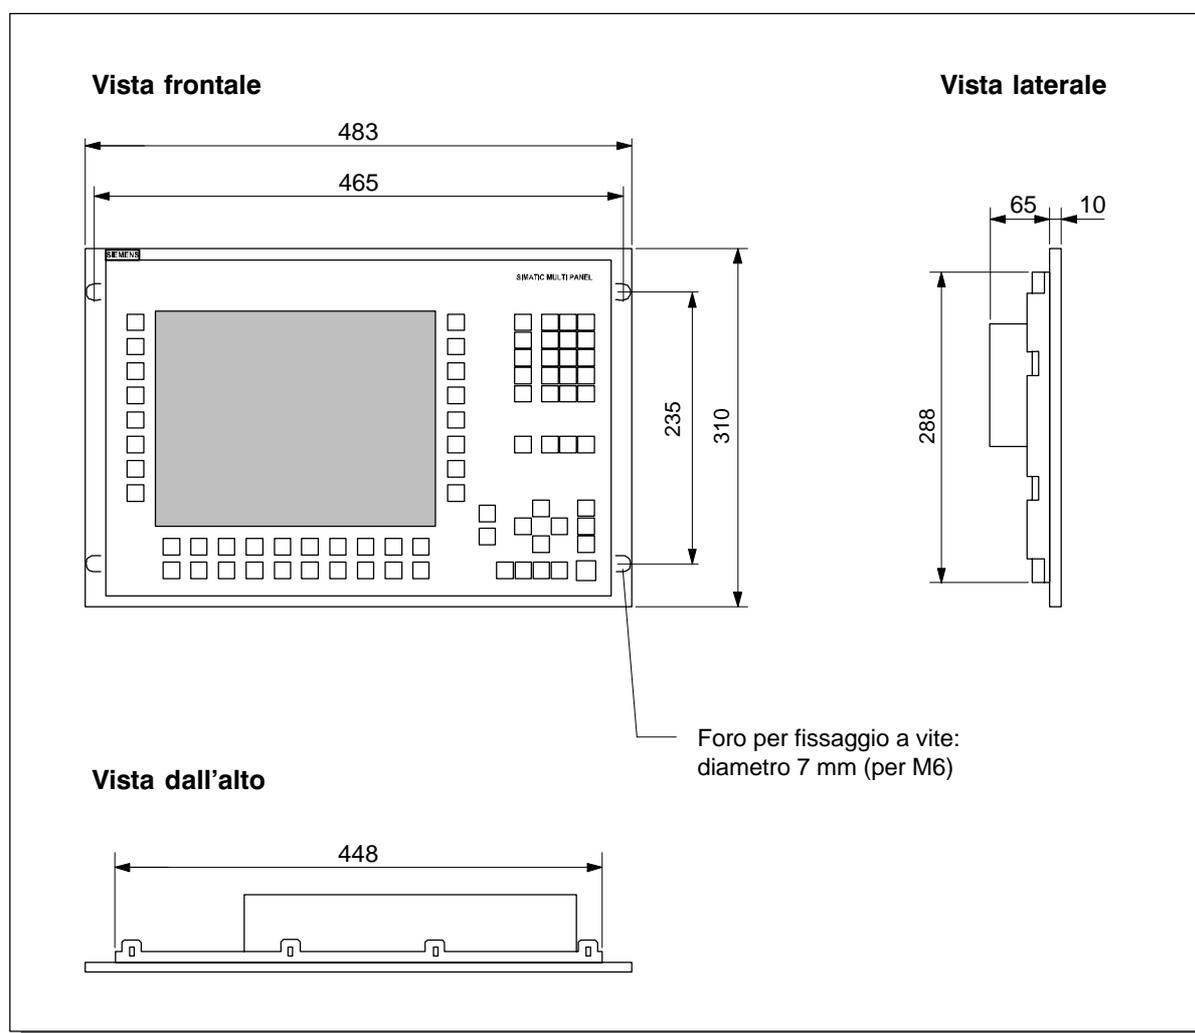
Dimensioni dell'apparecchiatura a tasti
